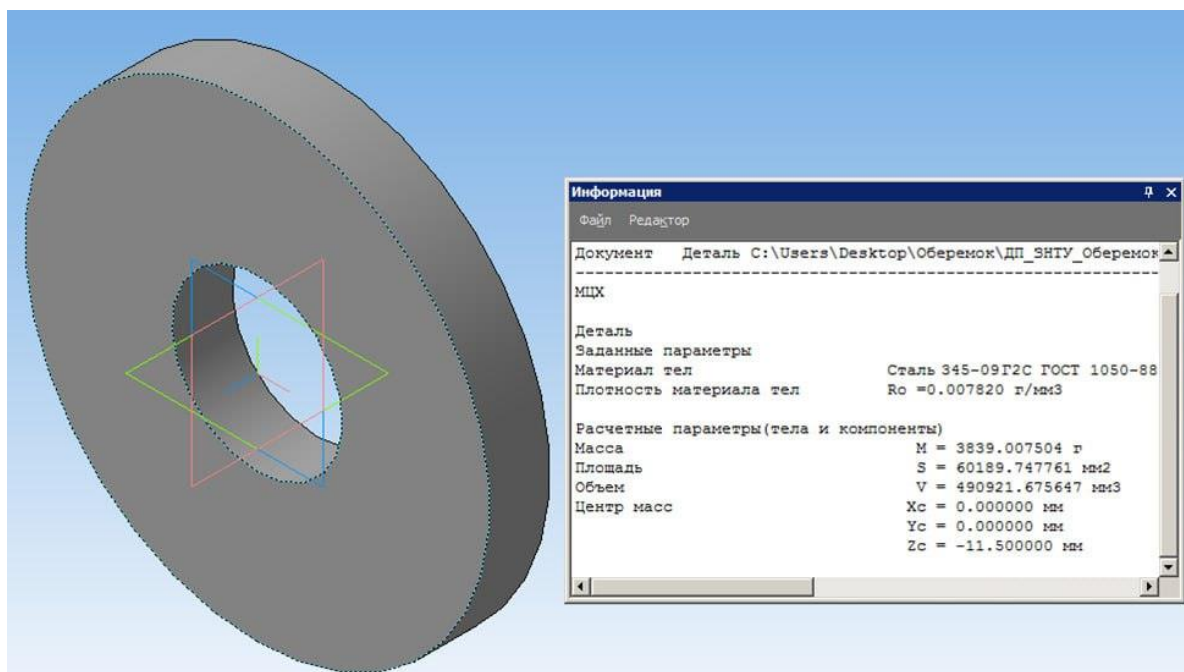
Тривимірна модель заготовки штамповка на молоті
